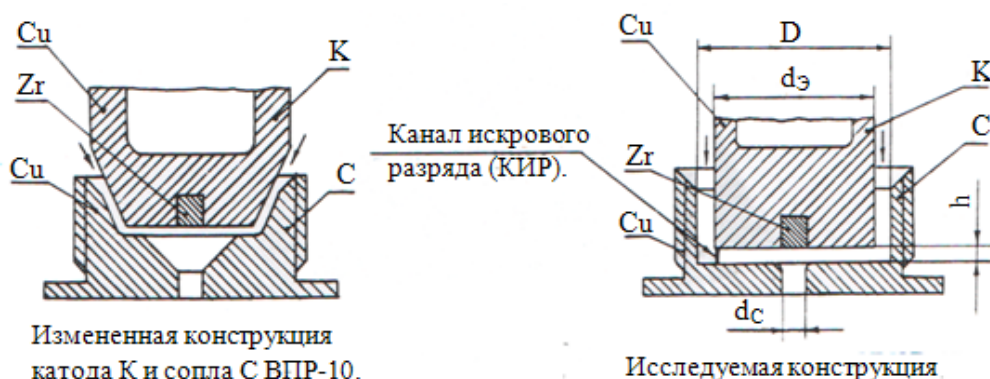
Измененные конструкции катода К и сопла С плазматронов
